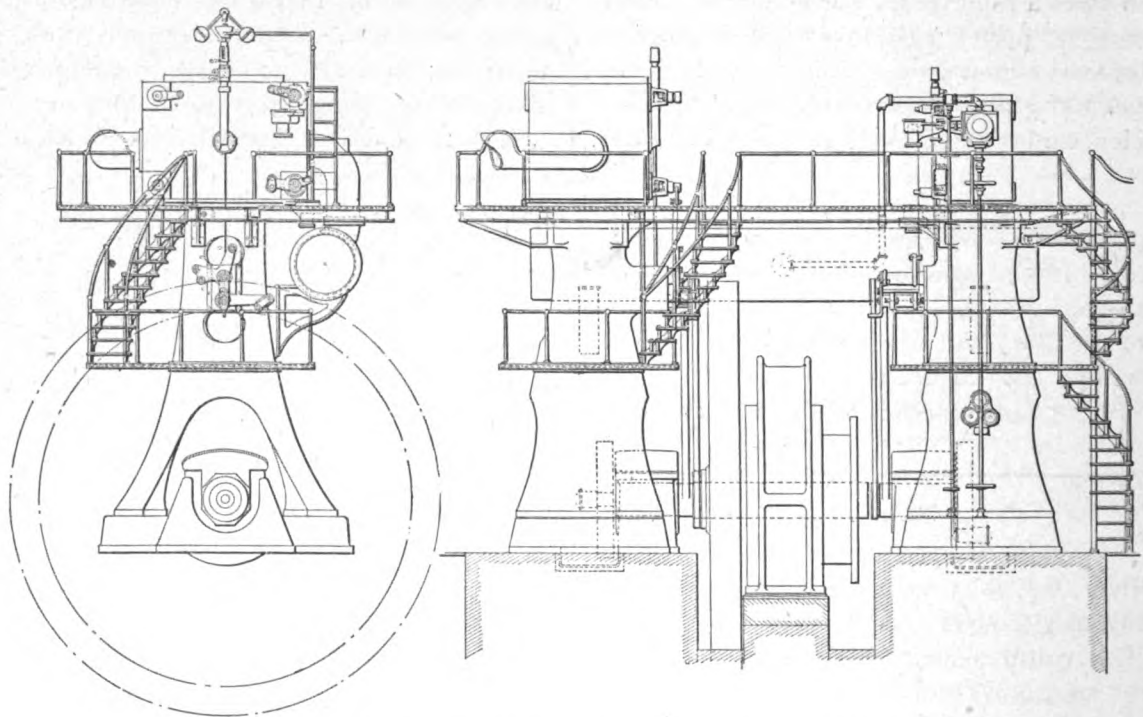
et 6. — Groupe générateur. Vue en bout et vue latérale.
